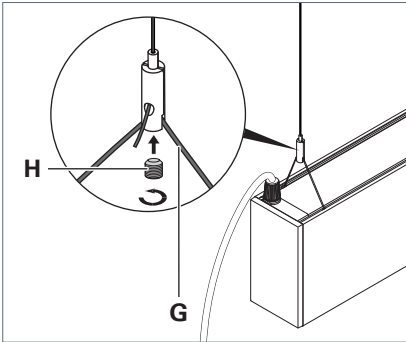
Leuchte an Drahtseilhalter befestigen.
